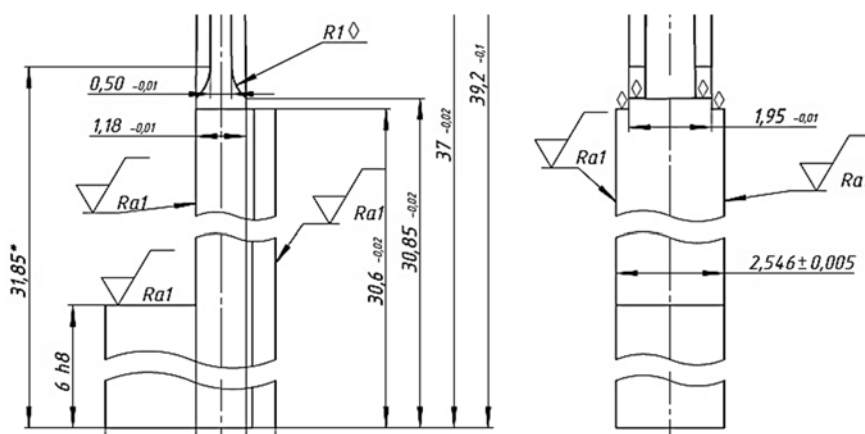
Фрагмент чертежа знака сборной формообразующей оснастки
